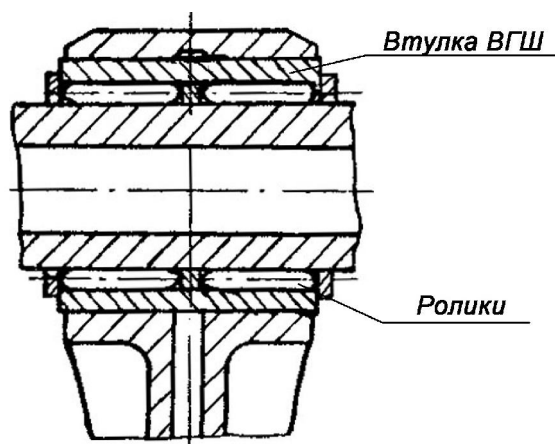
Подшипник ВГШ двигателя 5ТДФ
